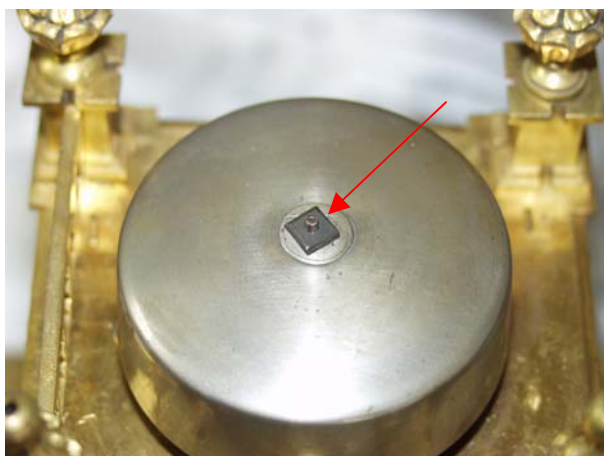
Aufstecken der Glocke und Befestigen mit Vierkantmutter (Pfeil)
